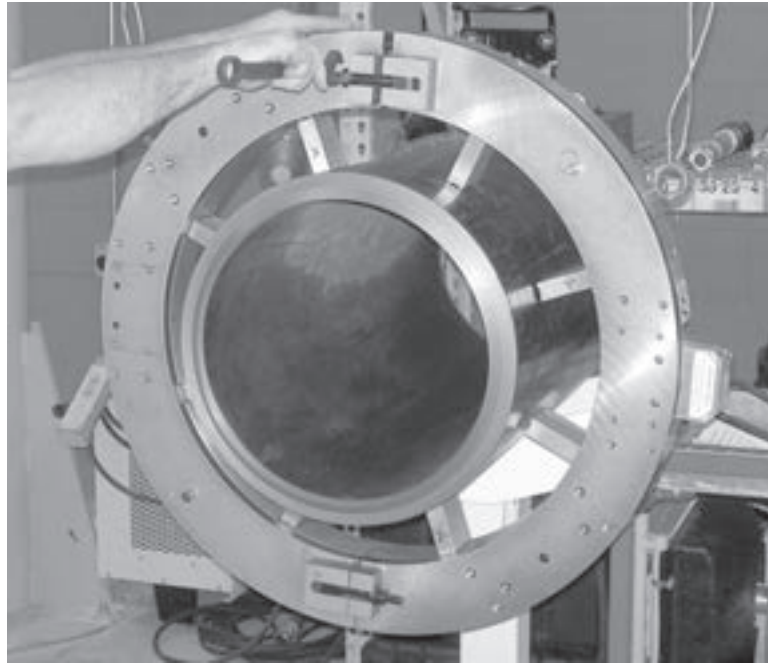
Ensamble las mitades de la máquina alrededor del tubo.
